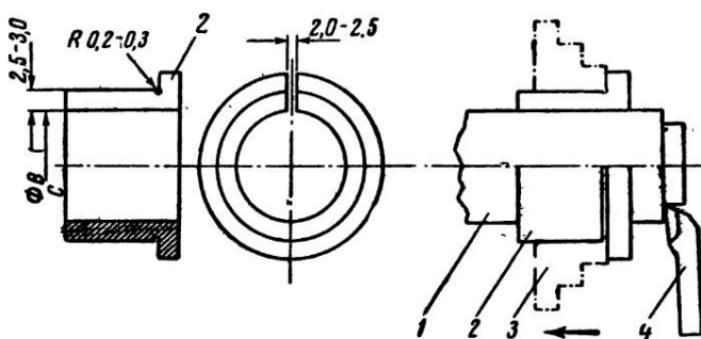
Разжимная втулка и ее применение: 1 — обрабатываемая деталь; 2 — втулка; 3 — кулачки патрона; 4 — резец.
